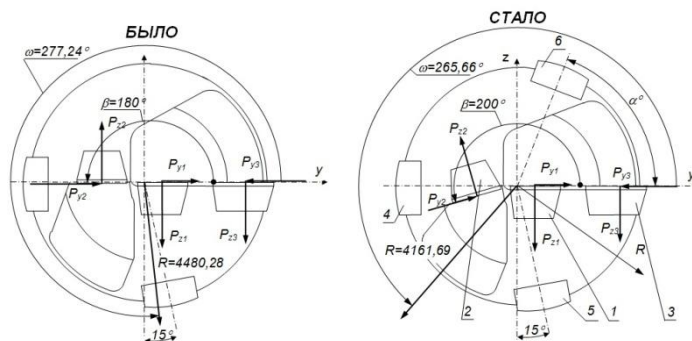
Схема новой конструкции инструмента для глубокого сверления отверстий
